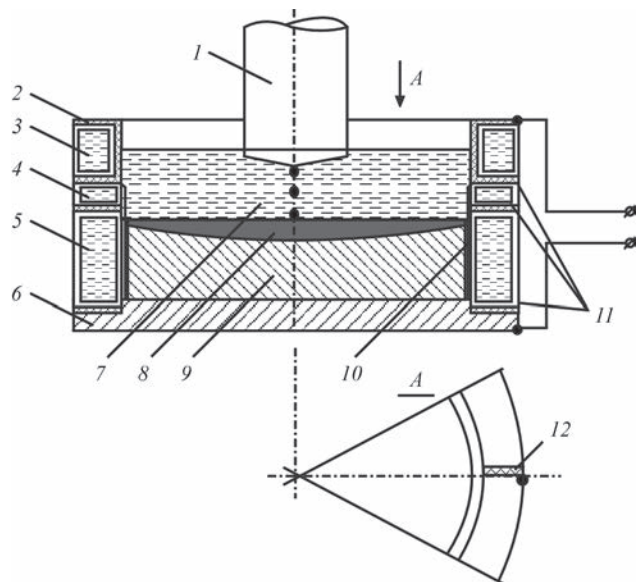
Схема ЕШН неструмоведучою заготовкою в СПК: 1 — заготовка, що переплавляється; 2 — графітова футеровка; 3–5 — струмопровідна, проміжна та формуюча секції відповідно; 6 — виріб; 7 — шлакова ванна; 8 — металева ванна; 9 — наплавлений метал; 10 — гарнісаж; 11 — ізоляційні прокладки; 12 — вертикальний паз з електроізоляційною прокладкою
